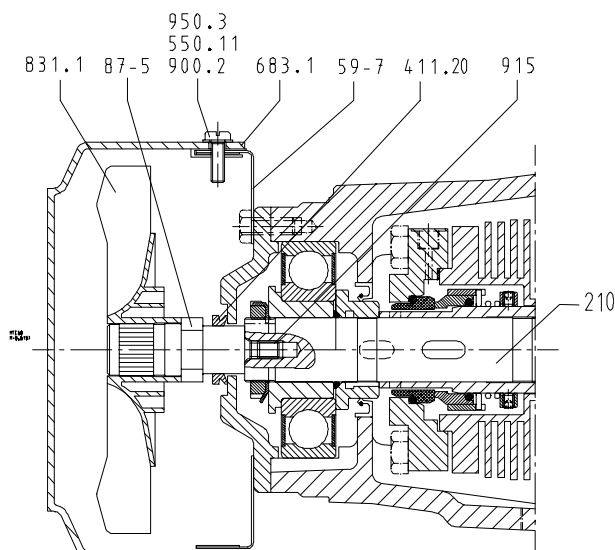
Desmontar o empanque mecânico refrigerado com ar - passos de desmontagem adicionais
